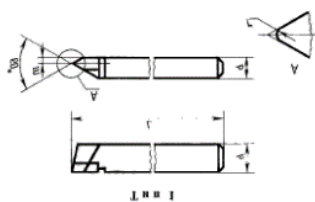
Геометрические параметры резца для метрической резьбы
